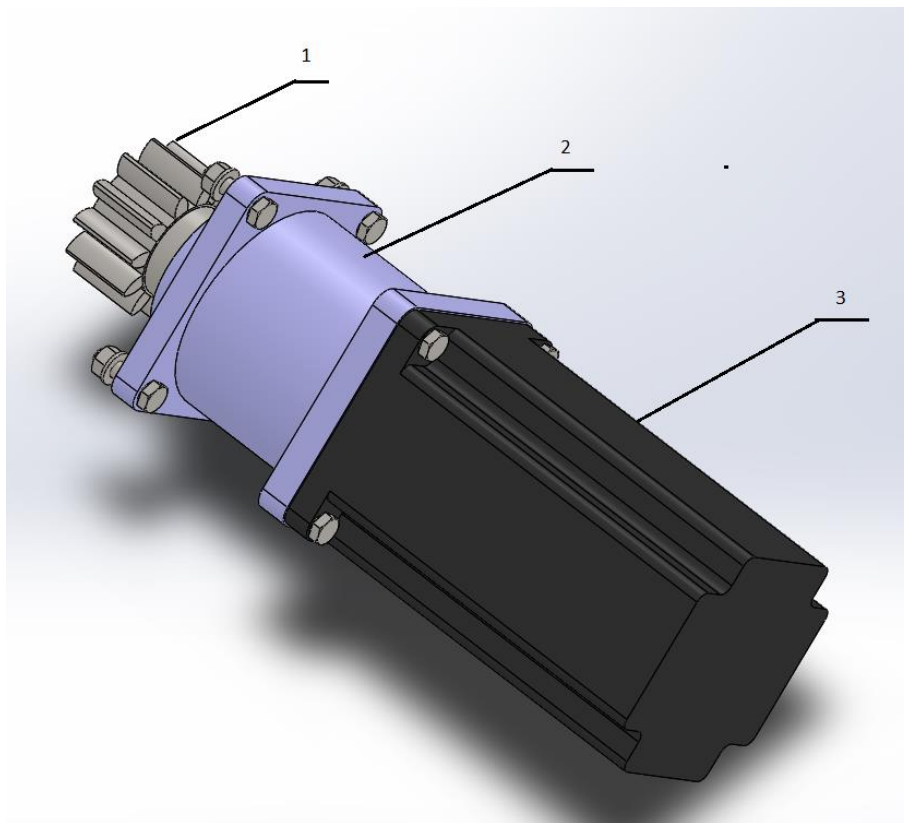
Тривимірний модель стандартних комплектуючих виконана в середовищі CAD SolidWorks
